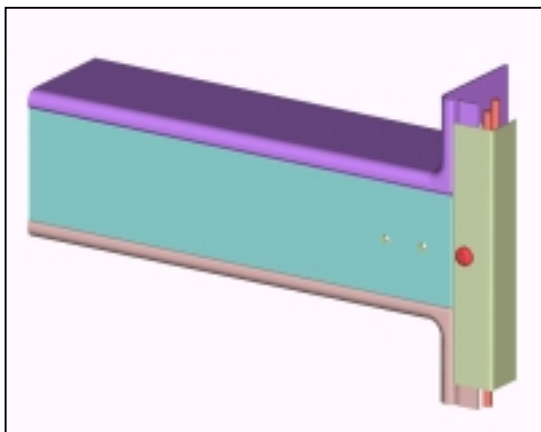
Figura A: Vista frontal da montagem do conjunto Travessa Intermediária.
